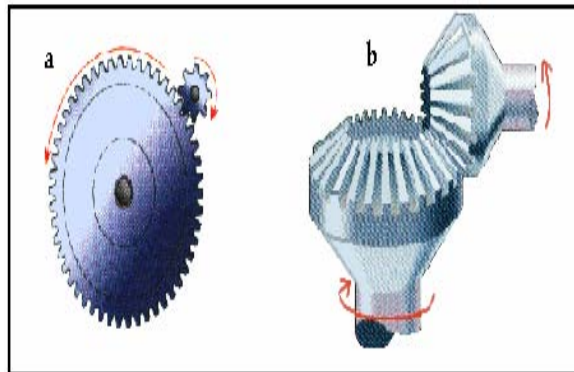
a) Engranés rectos b) Engranés cónicos
